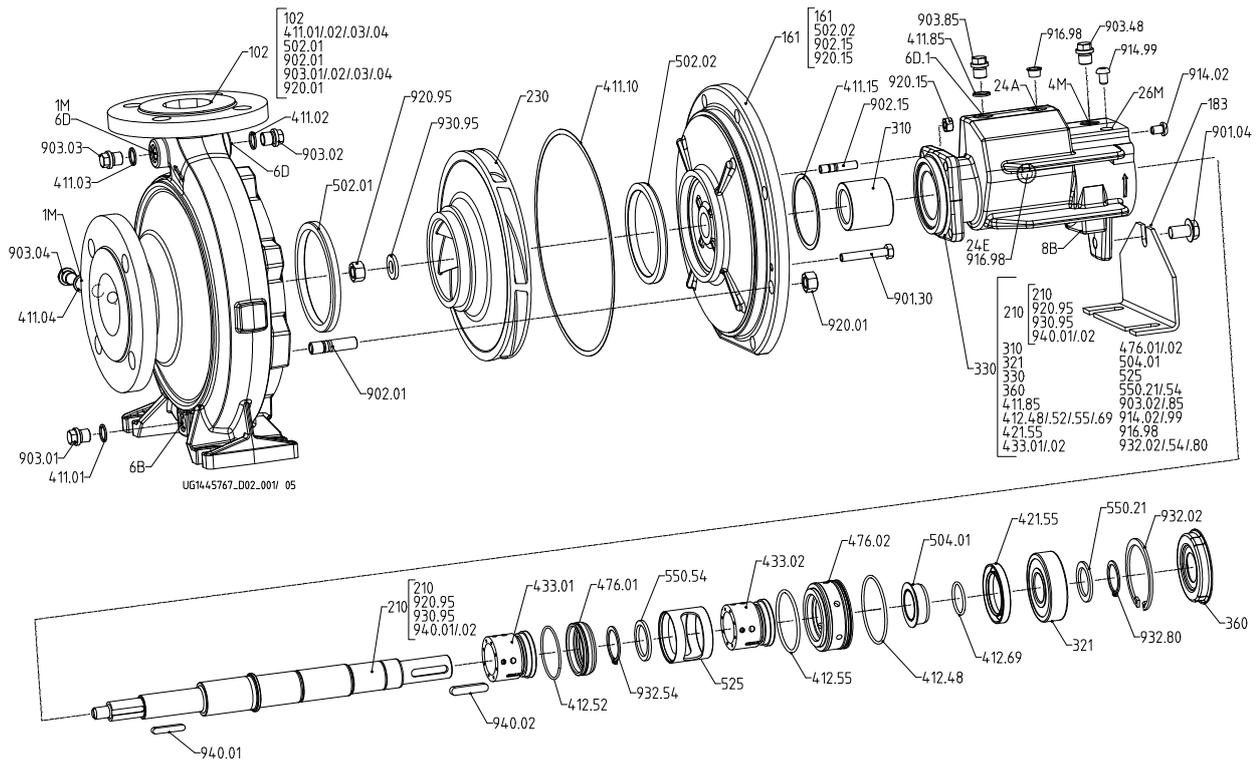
Vista detallada de Etanorm SYT, soporte de cojinetes WS_25_LS con cierre mecánico doble
